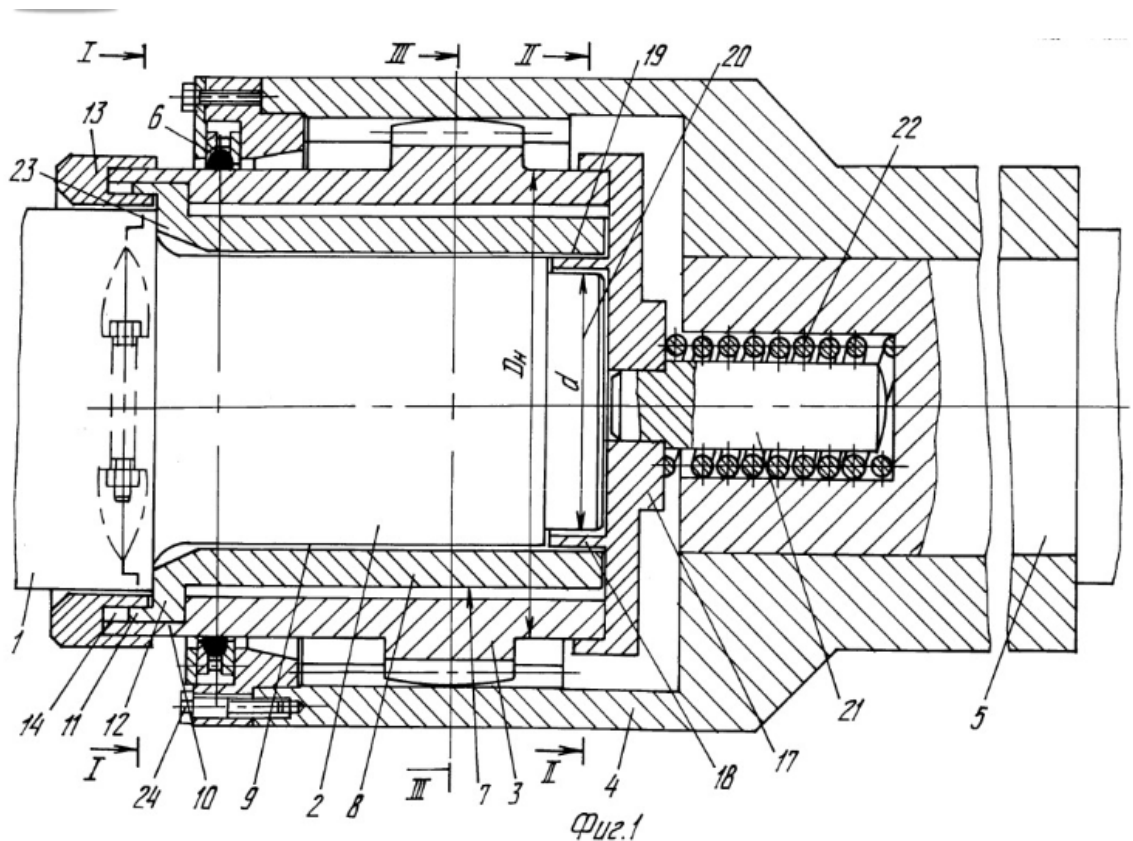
Вузол з'єднання прокатного валка зі шпинделем
